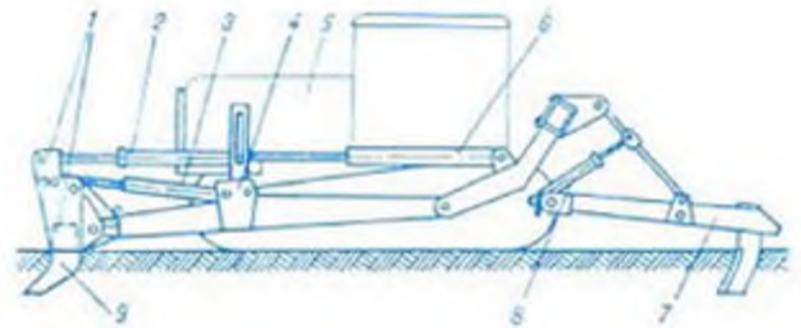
Корчеватель-сборатель КСП-20: 1 — корчевательное устройство; 2 — телескопическая тяга; 3 — гидроцилиндр поворота; 4 — рама; 5 — трактор; 6 — гидроцилиндр подъёма рамы; 7 — механизм подрезки корней; 8 — гидроцилиндр механизма подрезки корней; 9 — корчевательные клики.
